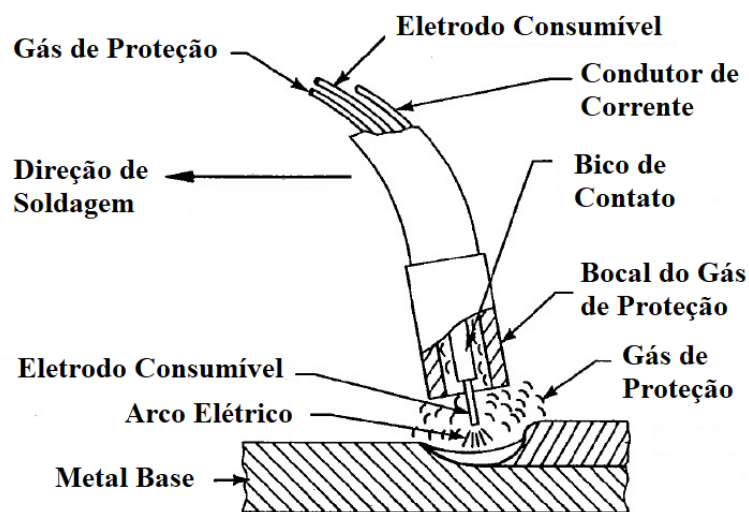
Esquema do processo de soldagem MAG [AWS, 2001].
